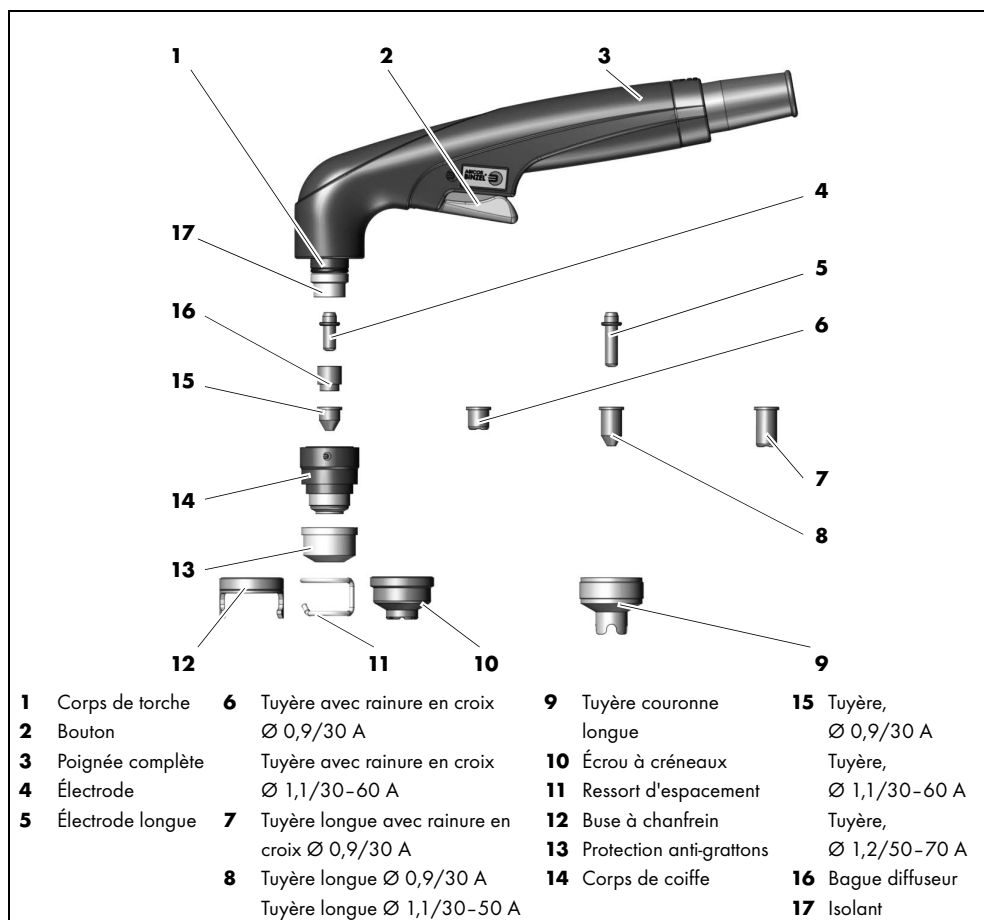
Vue d'ensemble d'ABIPLAS® CUT 71 HF
